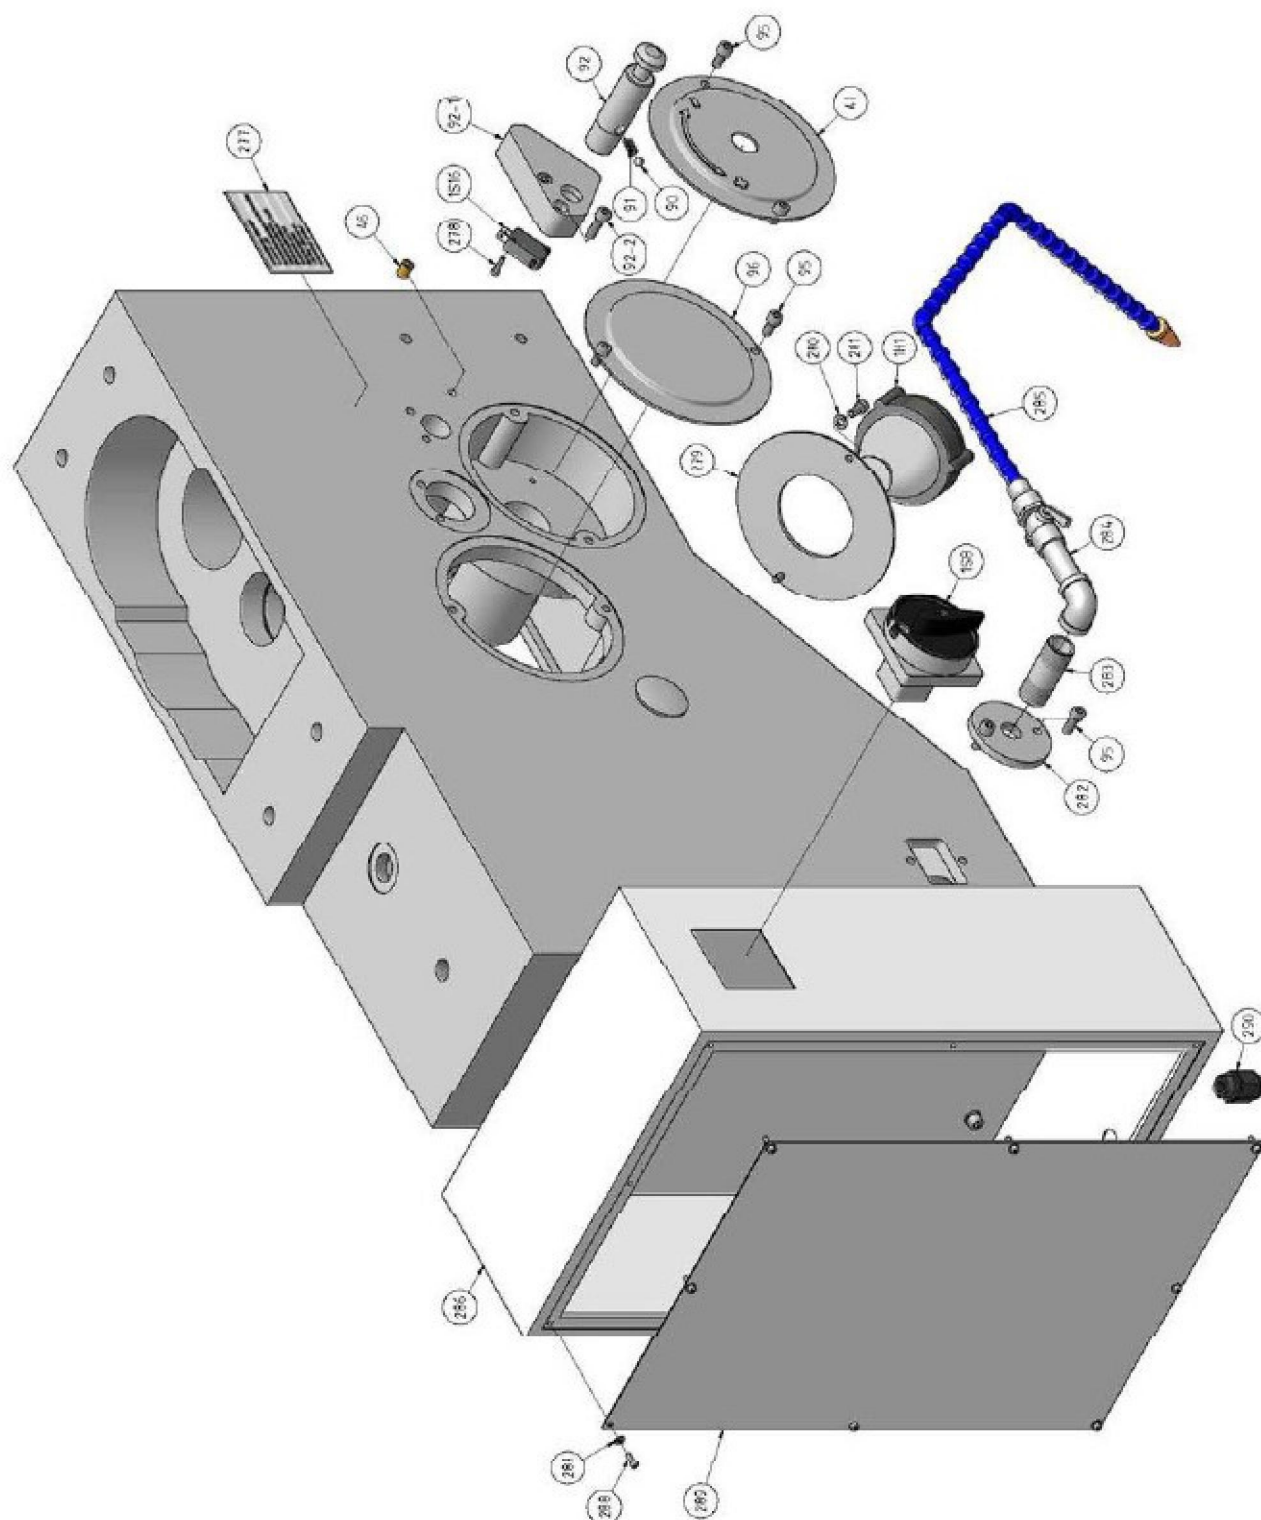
Caja de engranajes de avance 4 de 4 - Feed gear box 4 of 4
